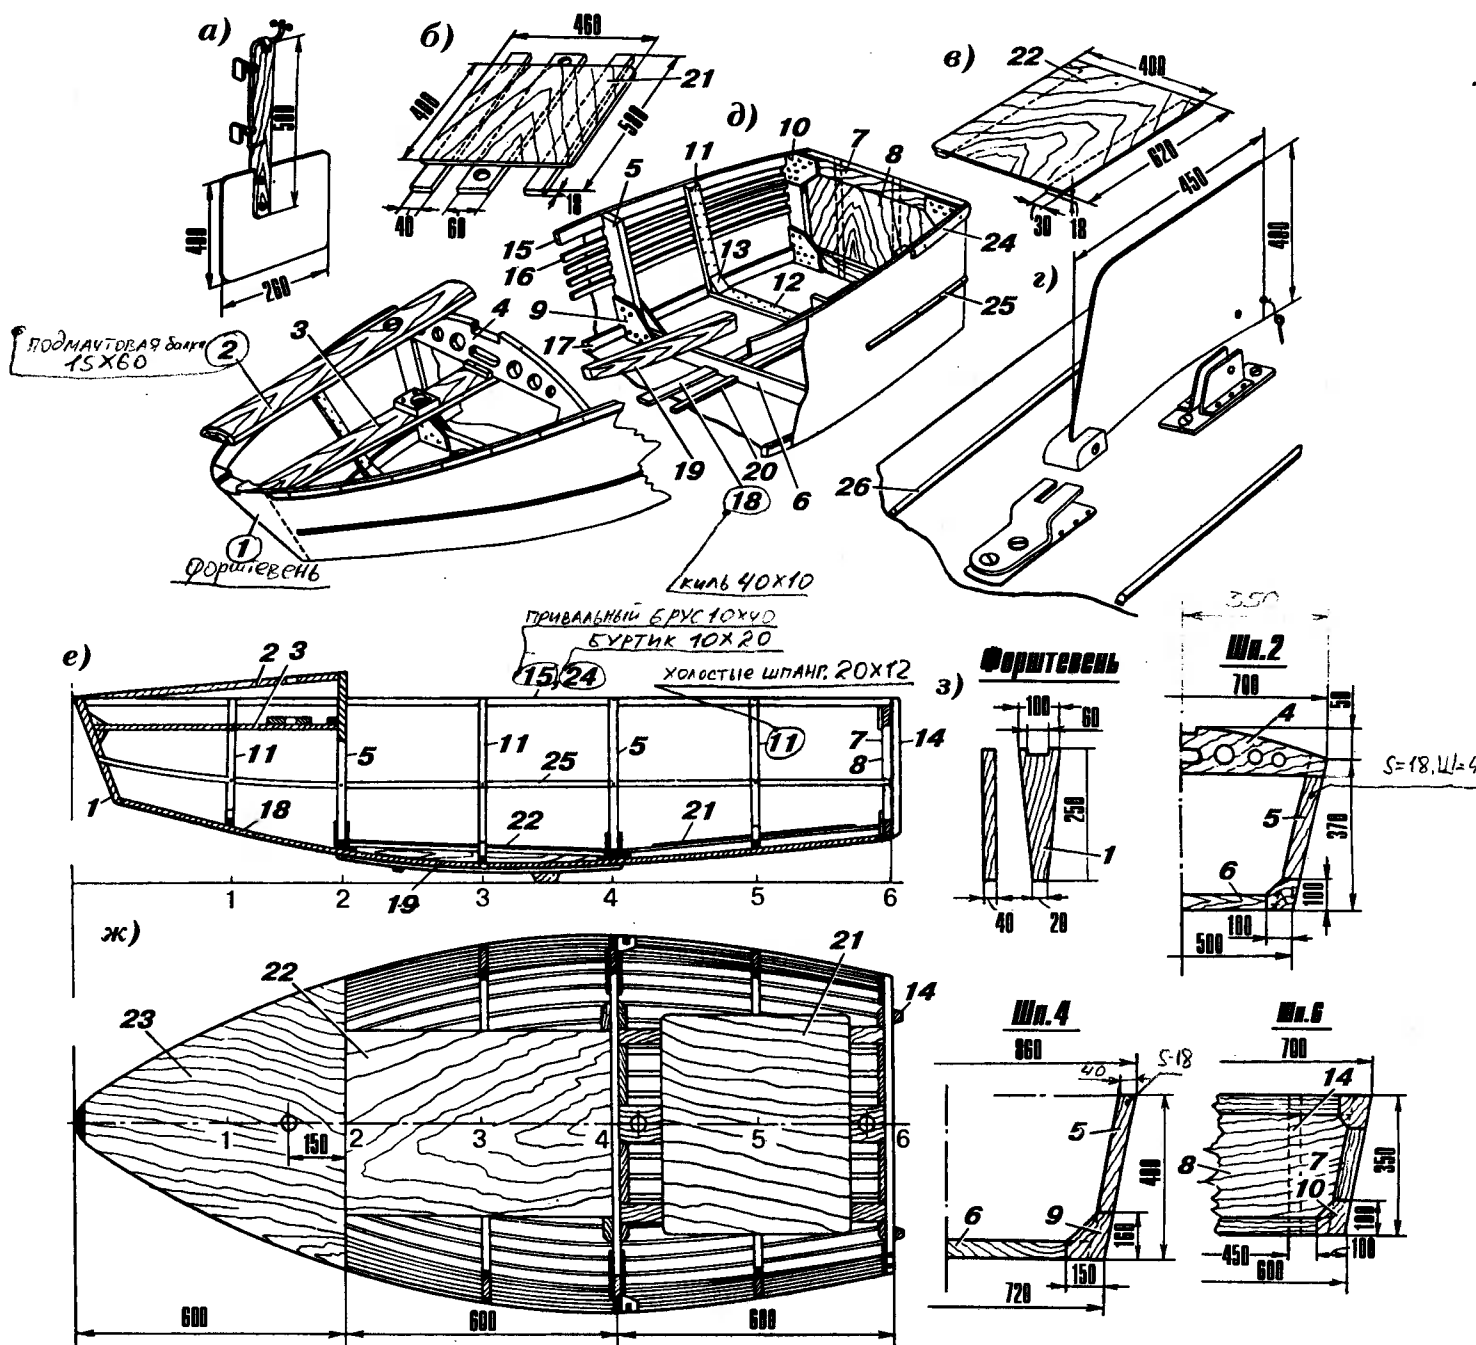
Устройство корпуса и детали (см спецификацию на с. 8) его оборудования:
